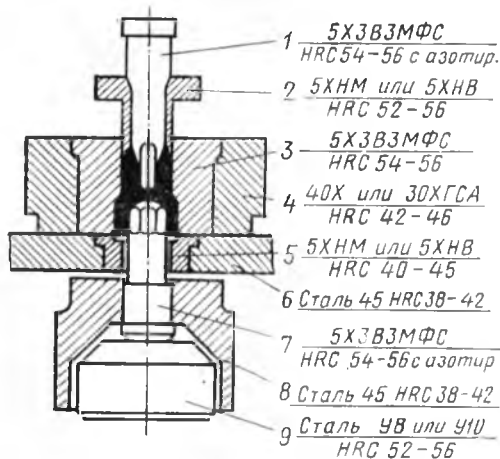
Марки стали и нормы твердости основных деталей штампа КГШП для полугорячего выдавливания поковки торцового гаечного ключа из стали 40Х:
